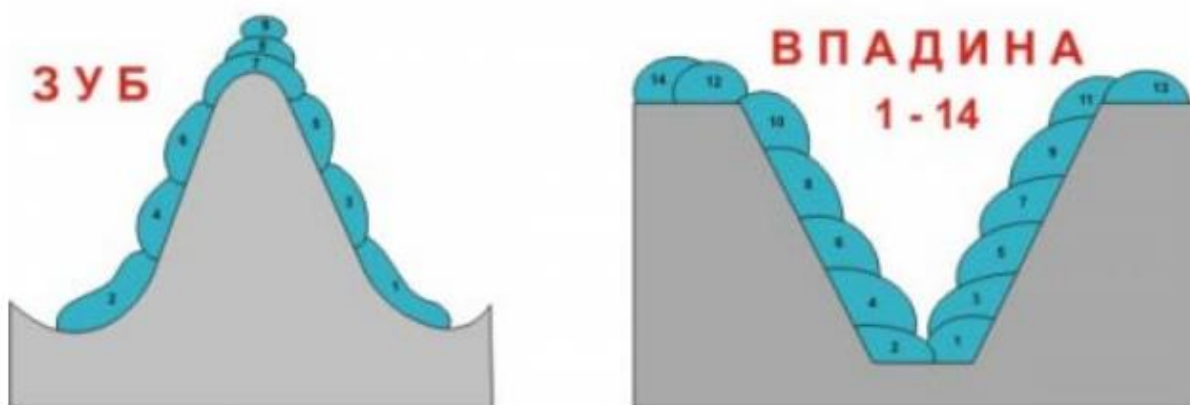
схема наплавлення шестерні, порядок накладання валів. [1]
